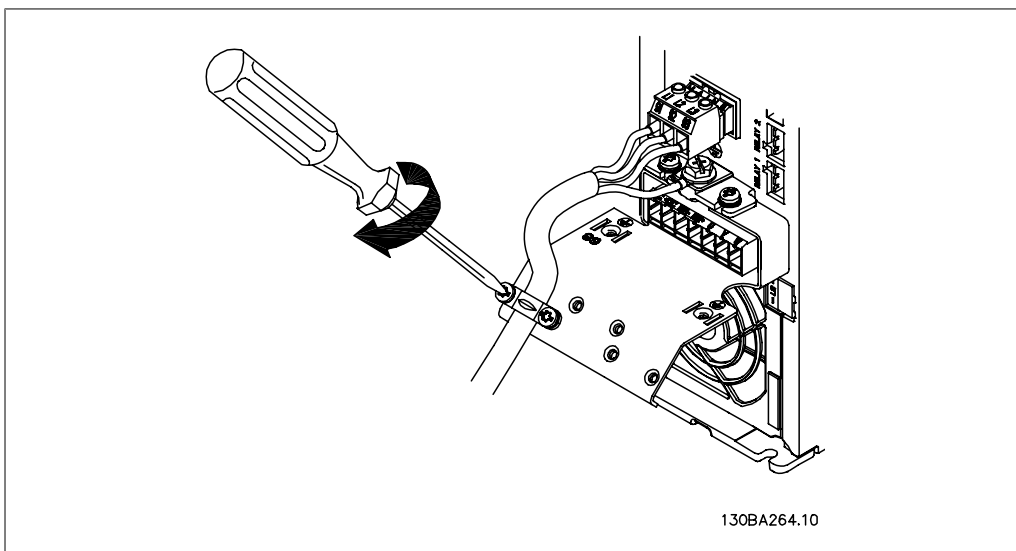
Por último, apriete la abrazadera de montaje de los cables de alimentación.
